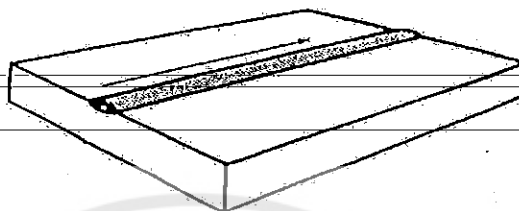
แสดงท่าเชื่อมที่เป็น Groove Weld ในงานเชื่อม Plate [2]
